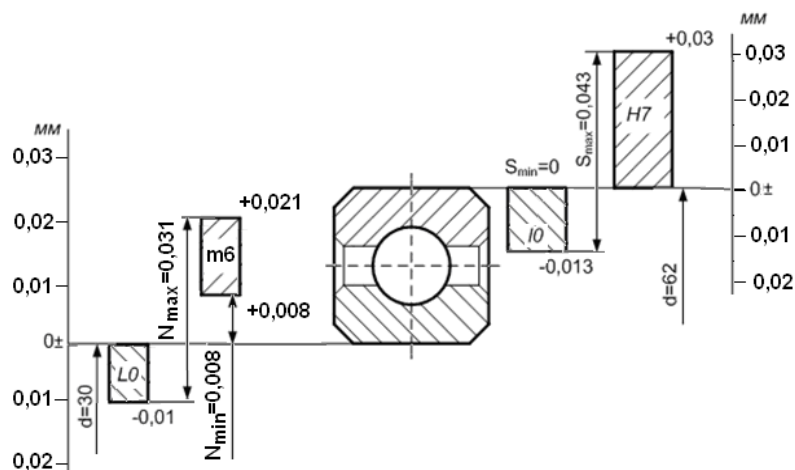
Схема розташування полів допусків кілець вальниці та посадочних поверхонь вала і отвору в корпусі
